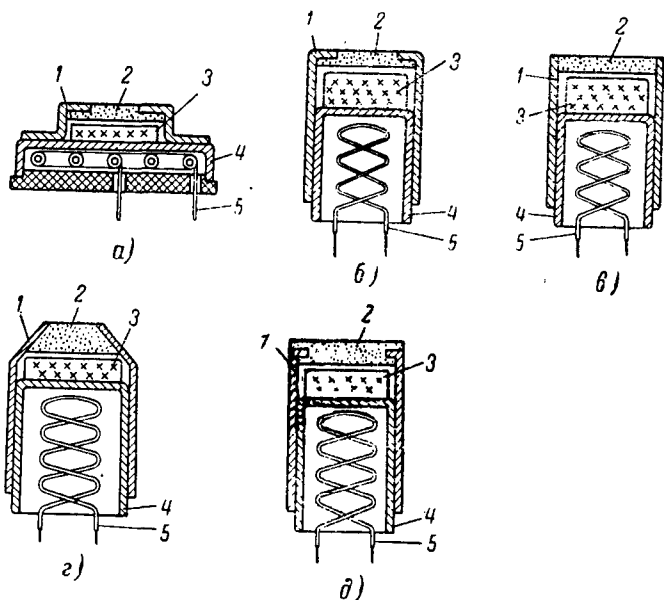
Катоды с различными формами деталей для запрессовки порошка.
